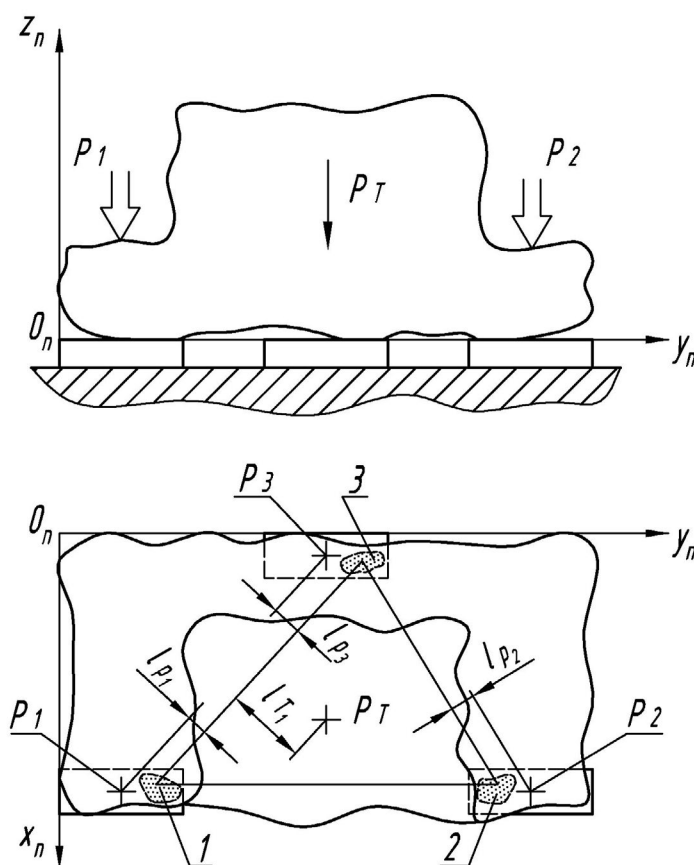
Условия появления опрокидывания заготовки при закреплении
